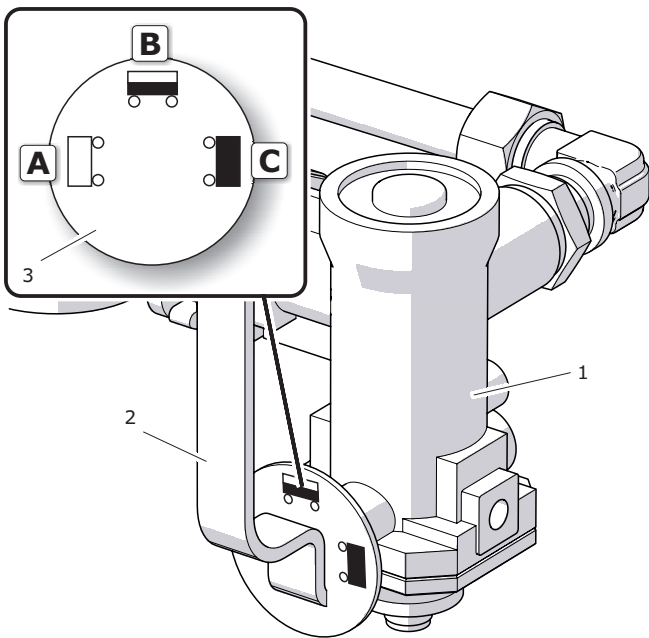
Regulador de fuerza de frenos de 3 posiciones
